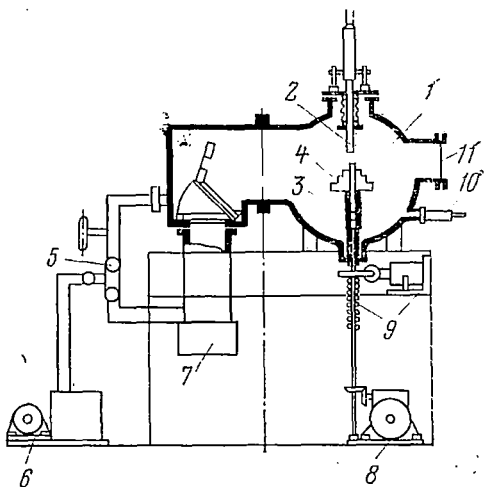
Схема установки для сварки электронным лучом в вакууме.
